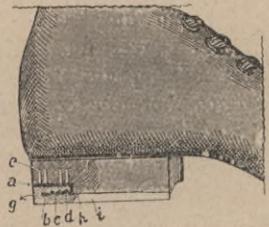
Die einfache Befestigungsart für Gummi-Laufsteck.
